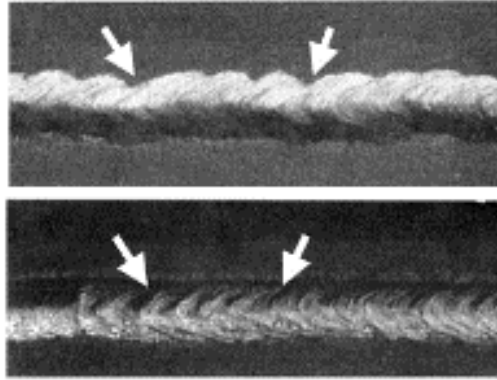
Ondas de cordón de soldadura desiguales.
